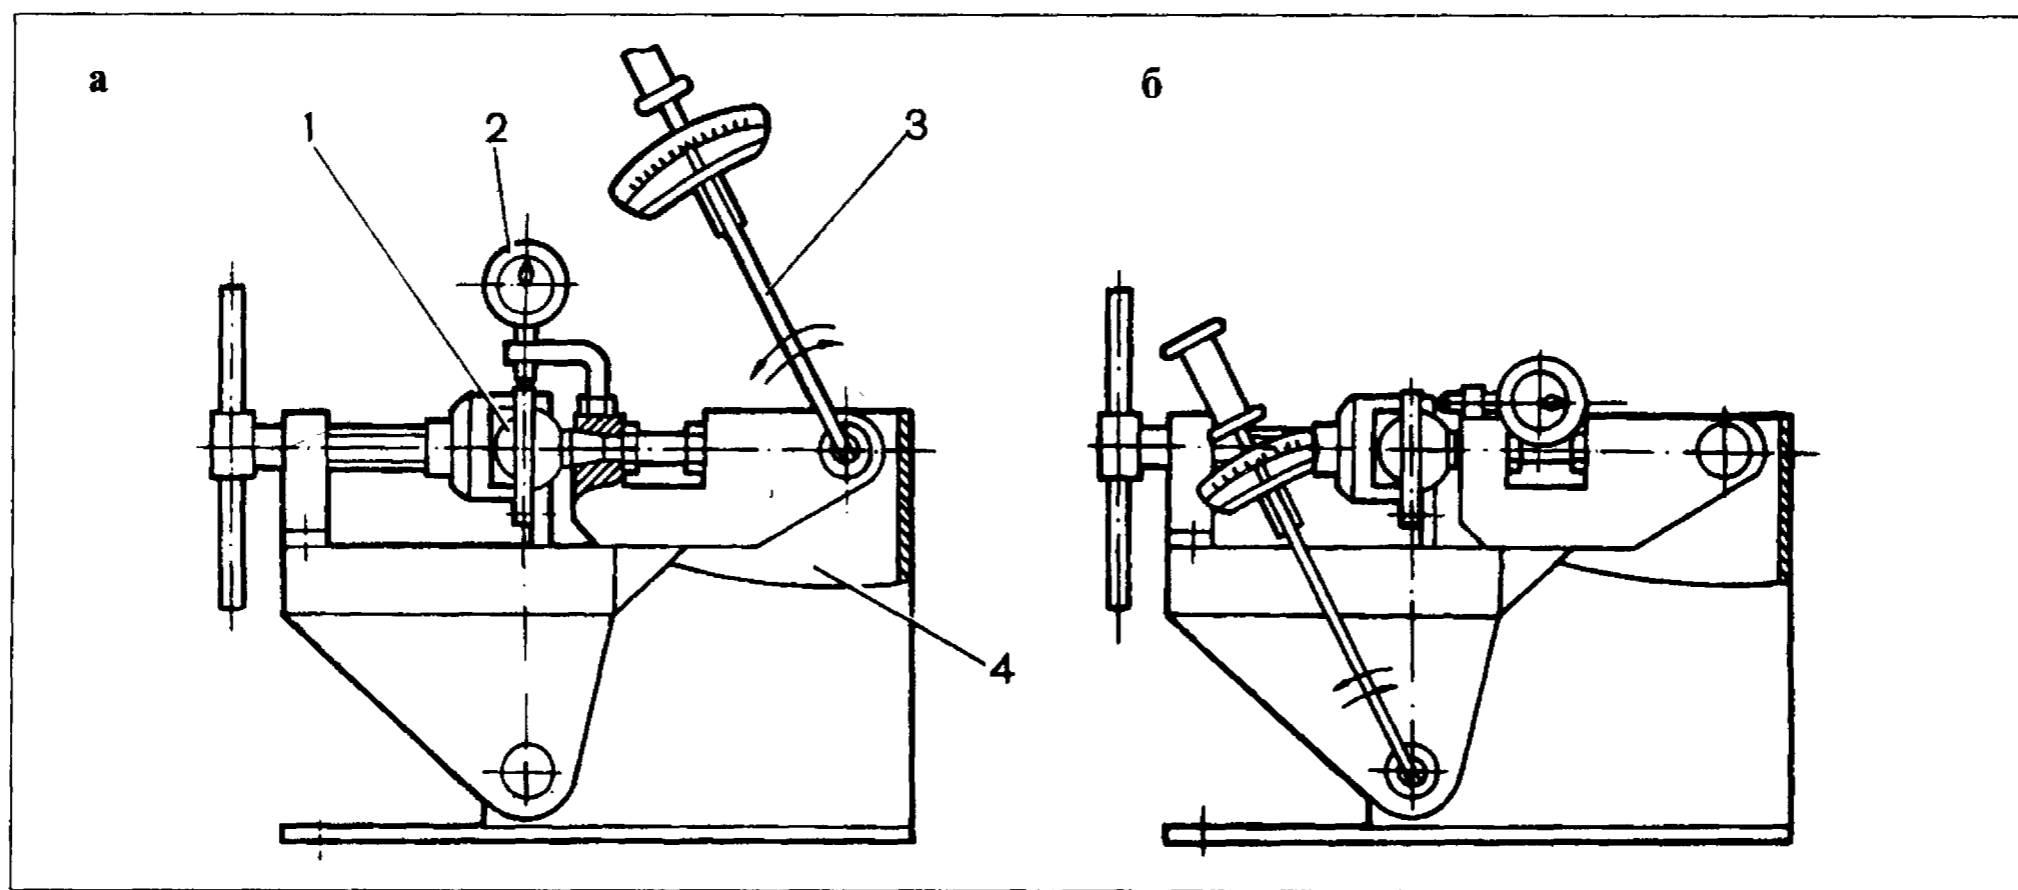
Проверка шарового шарнира на приспособлении 02.8701.9502:
